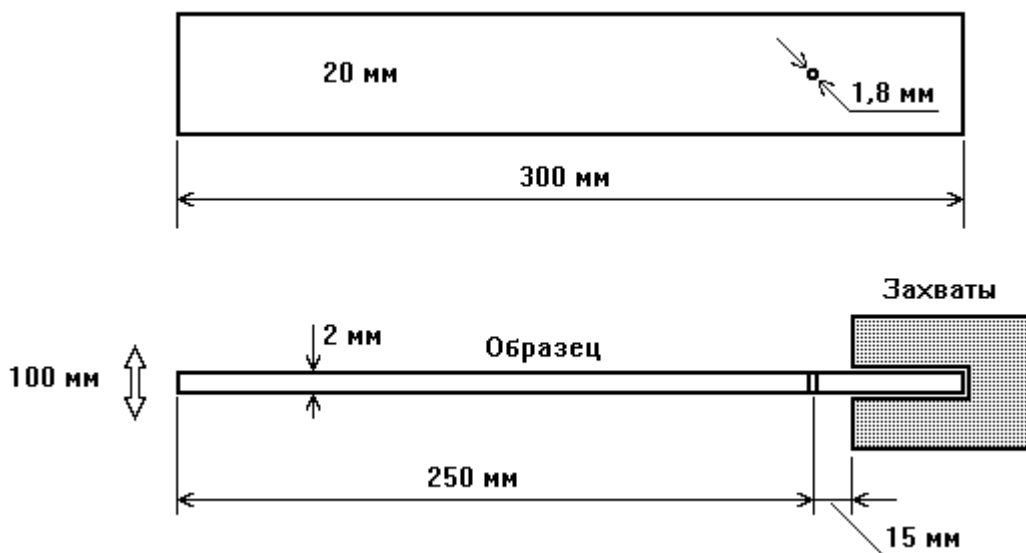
Вид и размеры плоских образцов, схема испытаний
